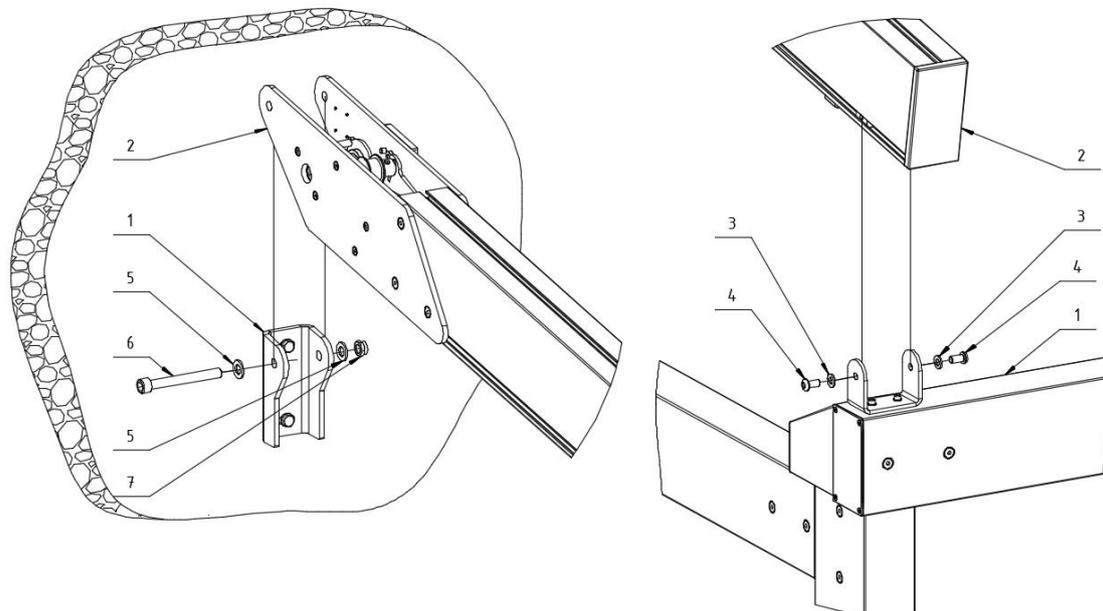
Méthode d'assemblage de la barre de guidage : 1 - Structure de support, 2 - Poutre de guidage, 3 Rondelle  $\varnothing 10,5$ , 4 - Boulon M10x20, 5 Rondelle  $\varnothing 15$ , 6 - Boulon M14x120 / M14x220, 7 - Ecrou M14.
